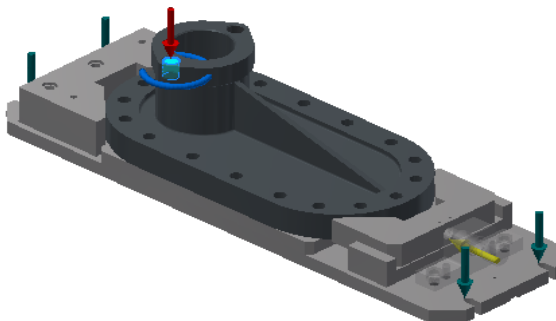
Действие осевой силы резания инструмента (красная стрелка), крутящего момента (синяя стрелка) на заготовку детали «Опора», закрепленной в приспособлении при механической обработке отверстия
